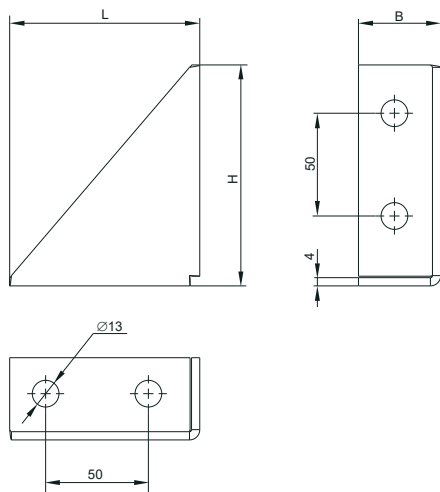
Уголок крепежный двойной усиленный для STRUT-профиля / Figure F.3 – Double reinforced fastening angle for STRUT profile
